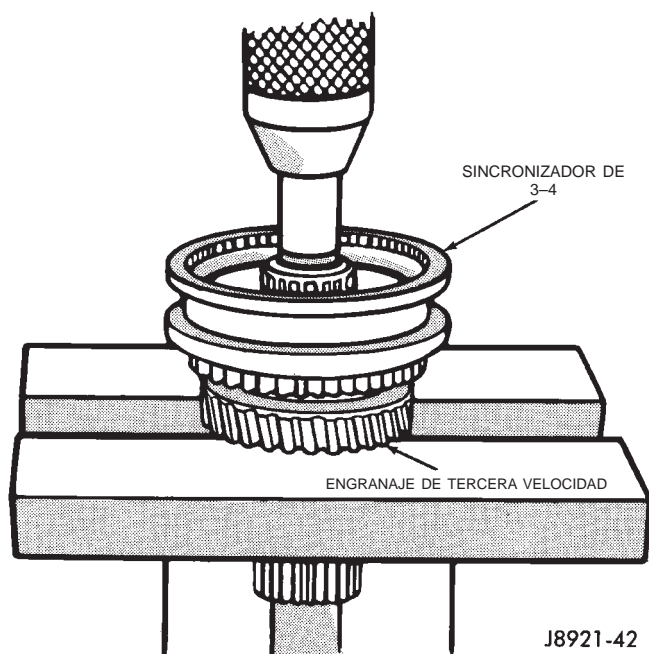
Desmontaje de sincronizador de 3-4 y engranaje de tercera velocidad
